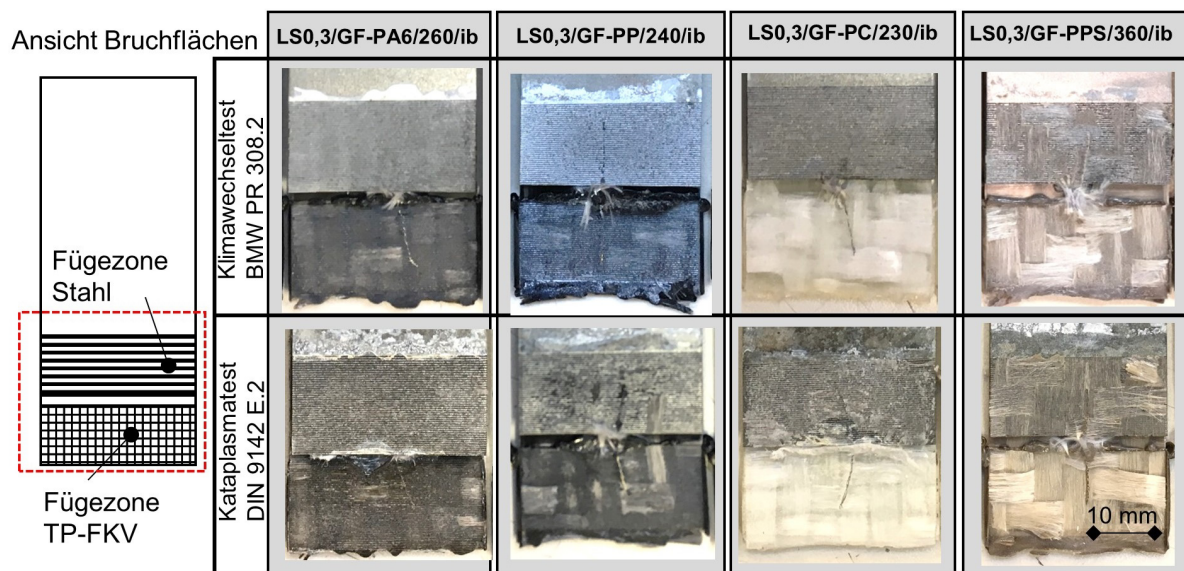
Bruchflächen geprüfter Zug-Scher-Proben nach den Witterungstest BMW PR 308.2 und Kataplasma Test nach DIN 9142E.2
